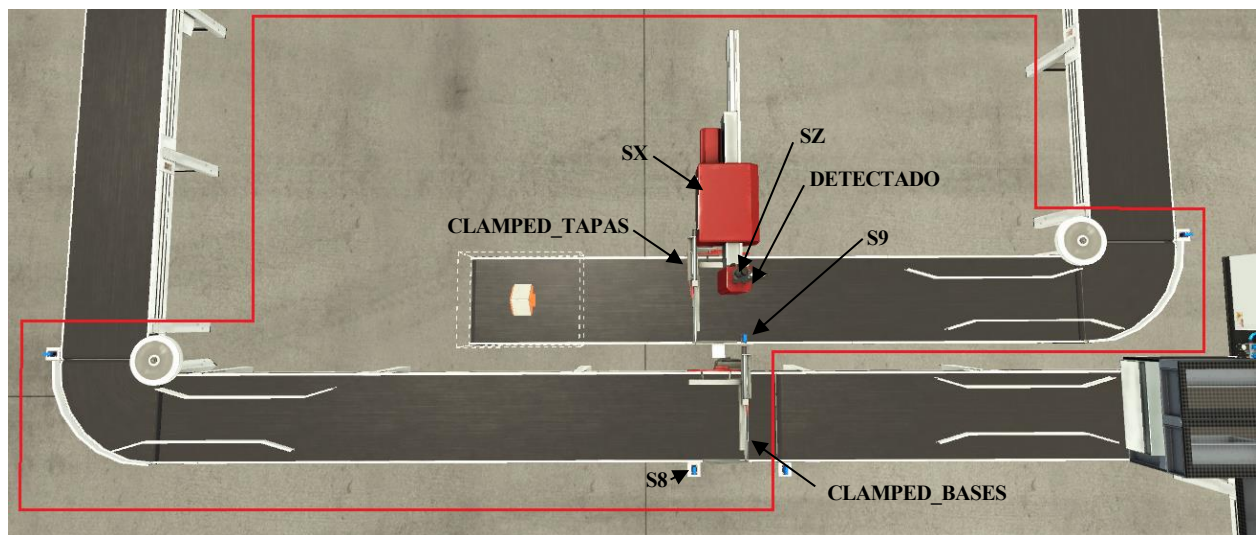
Ubicación en planta de los sensores de la estación de ensamblaje.
